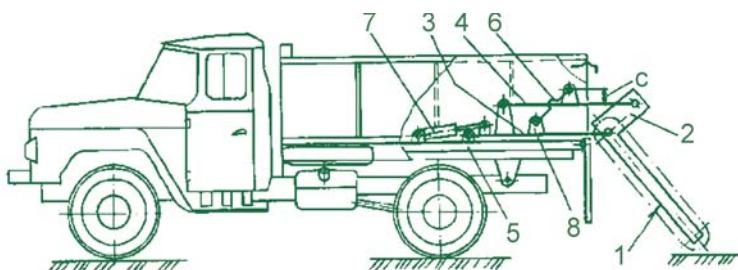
Схема навесного перегрузочного устройства для автомобиля в рабочем положении (без рольганга), вид сбоку (патент на полезную модель № 93754)
